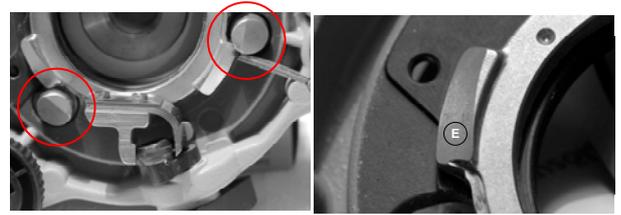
+b - Vista detallada (desde abajo) de la placa superior de la brida nivelante que muestra el instrumento suelto (a); Vista detallada de la brida de fijación (b)
